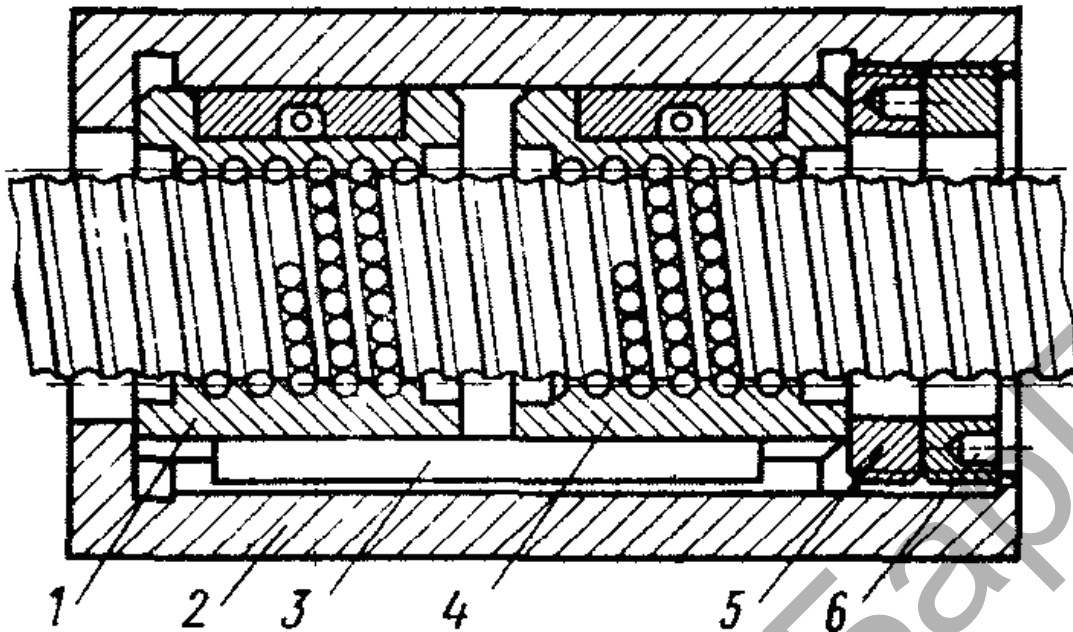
Конструкция передачи винт-гайка качения
